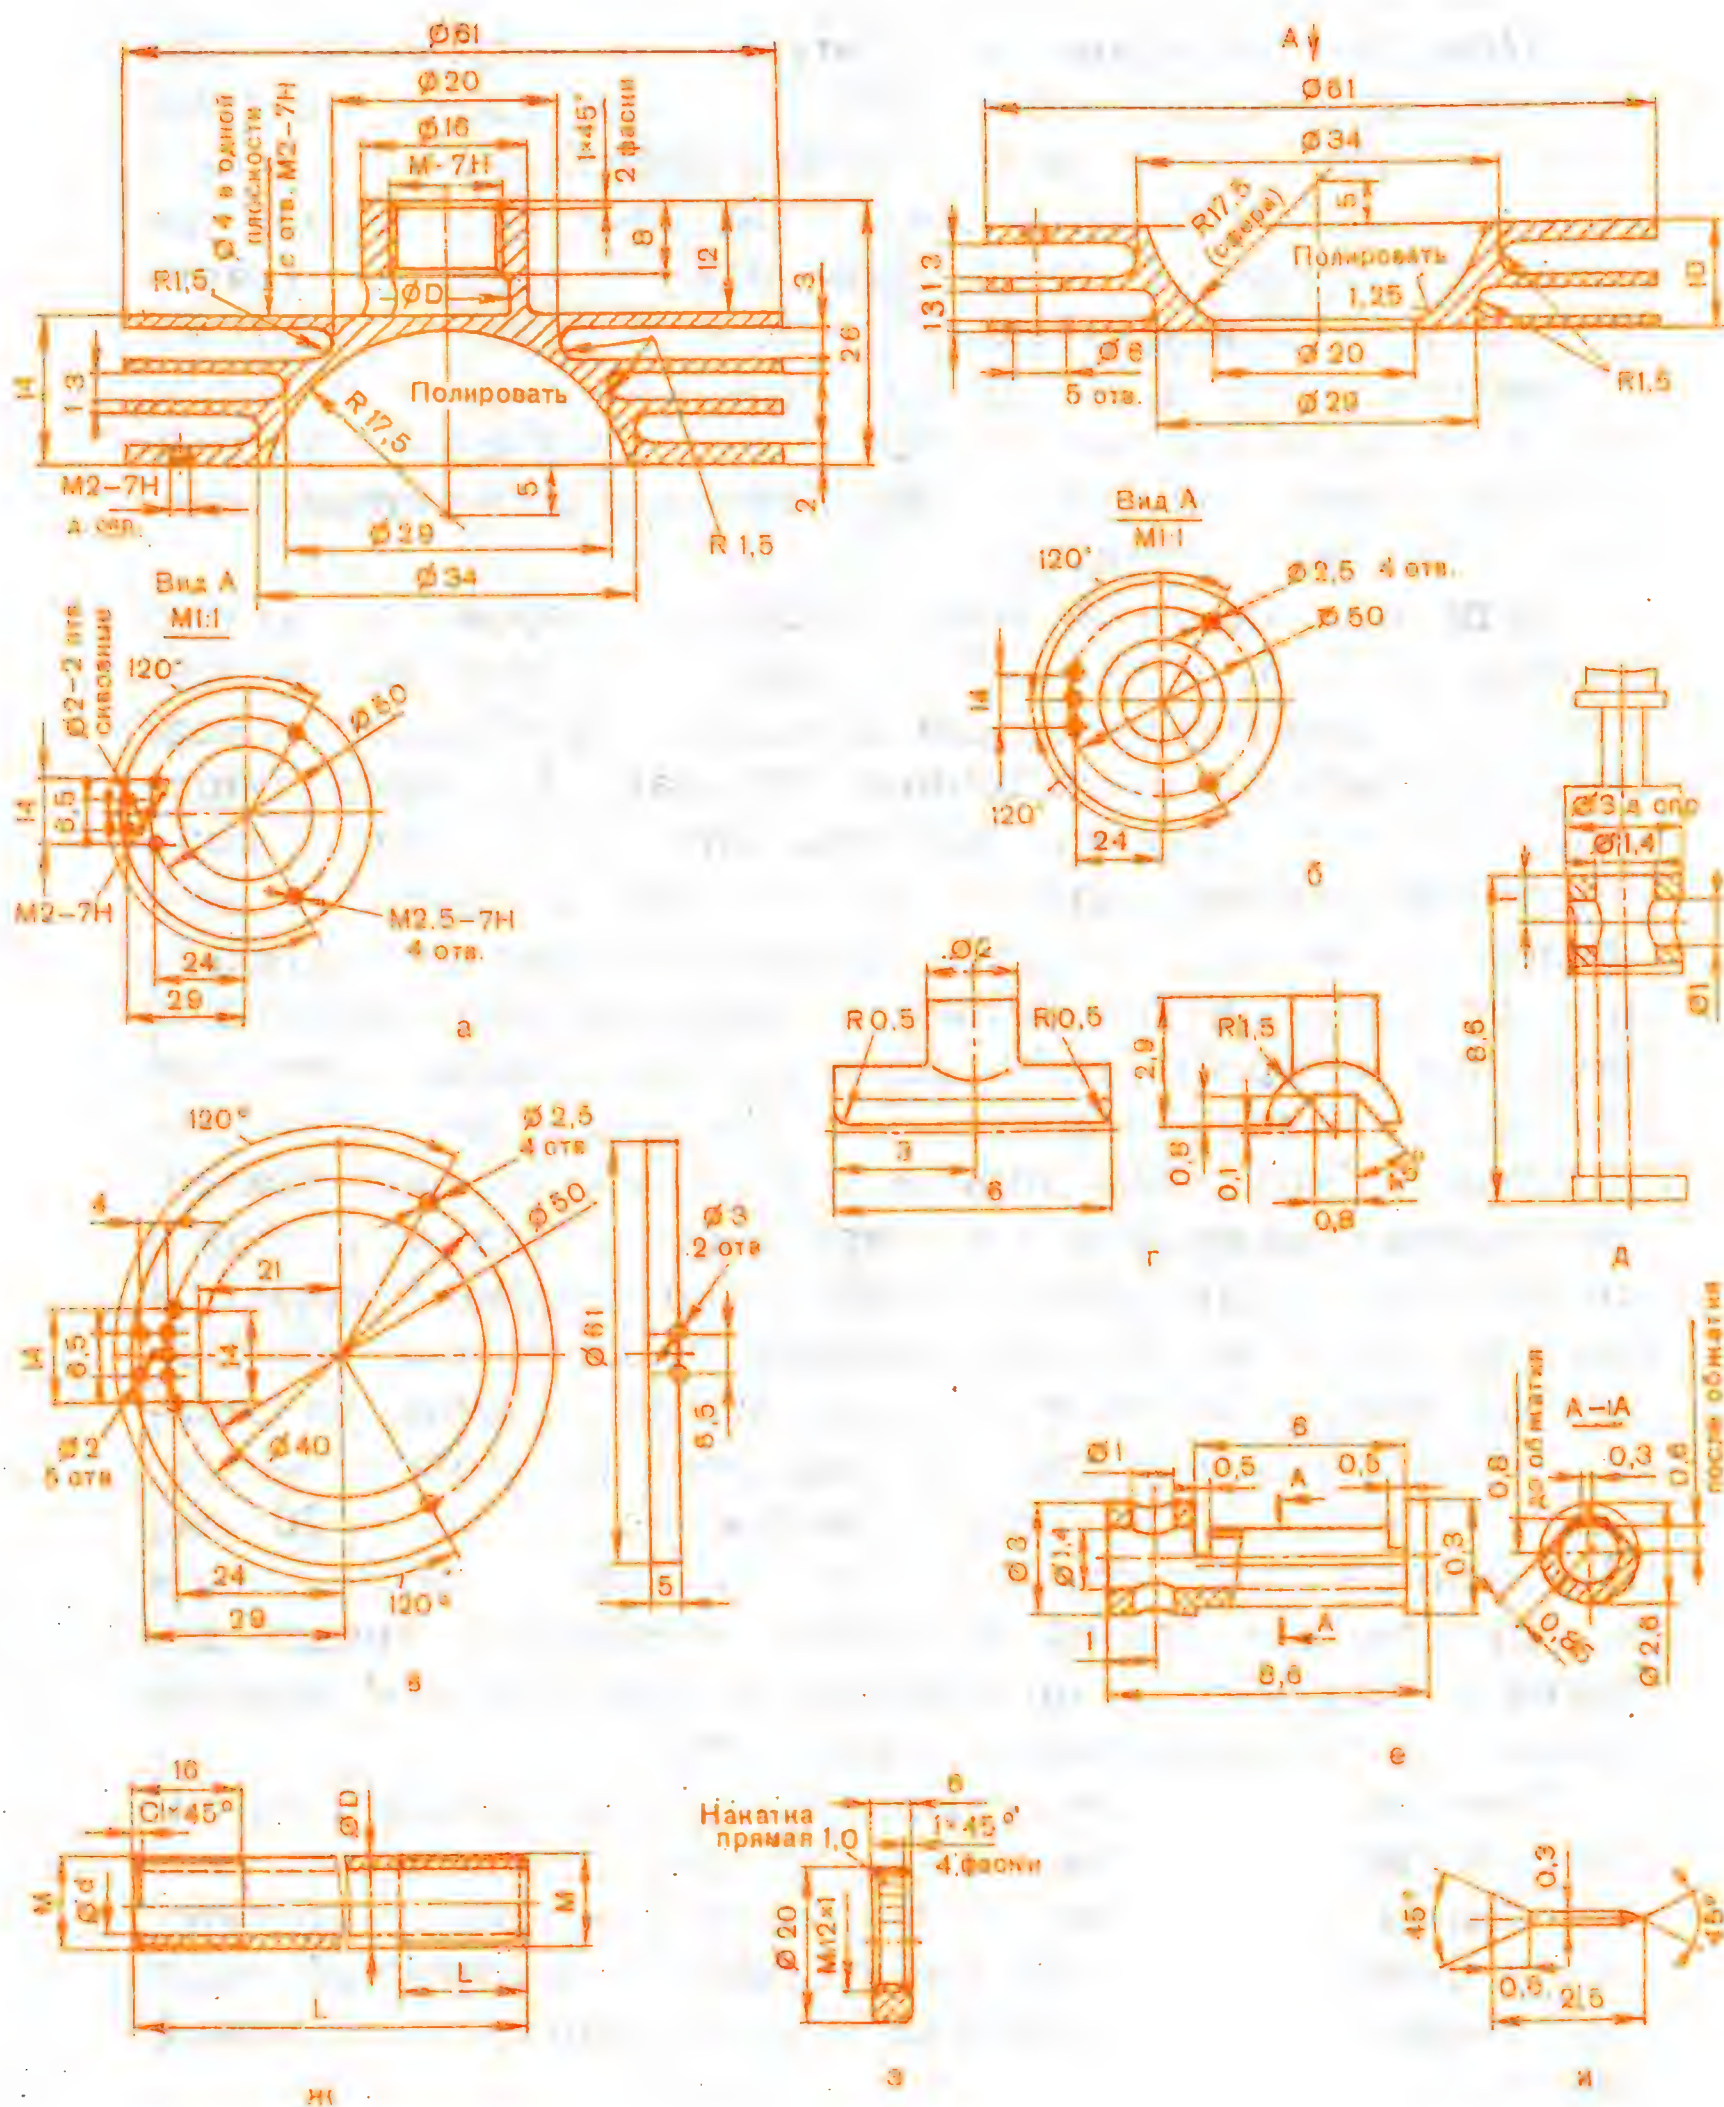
Детали осветительного устройства: а — верхняя крышка корпуса, б — нижняя крышка корпуса, в — прокладка электротеплоизоляционная, г — стопор, д — гнездо, после доработки готового изделия, е — гнездо, изготовленное заново, ж — трубчатая державка, з — гайка круглая, и — штифт
